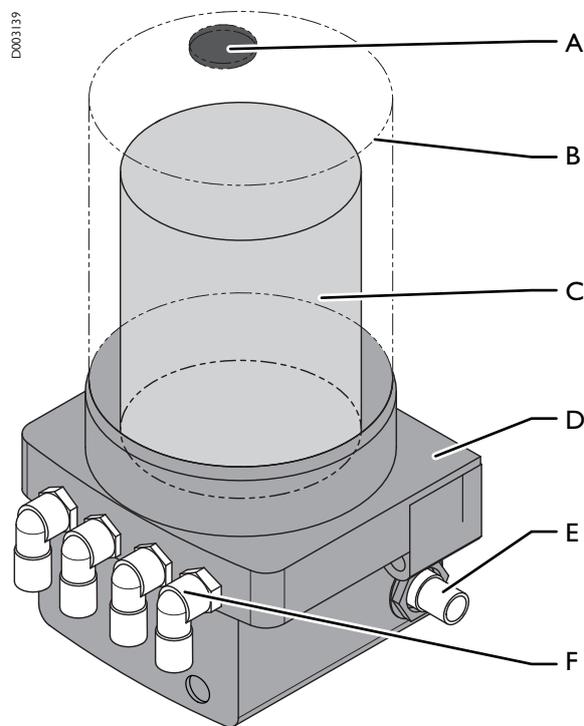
Детальная конструкция FlexxPump 404DLS
